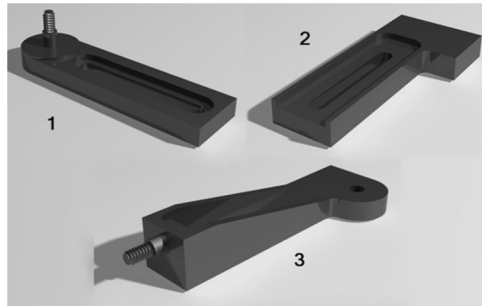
3D модель деталей: 1 – верхня направляюча; 2 – нижня направляюча; 3 – вертикальна стійка
